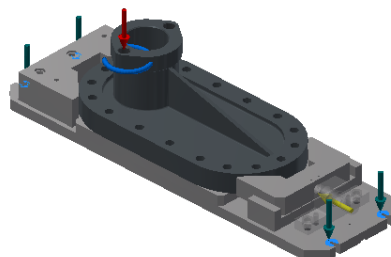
Действие усилия закрепления приспособления на столе станка при механической обработке отверстия в заготовке детали «Опора»
